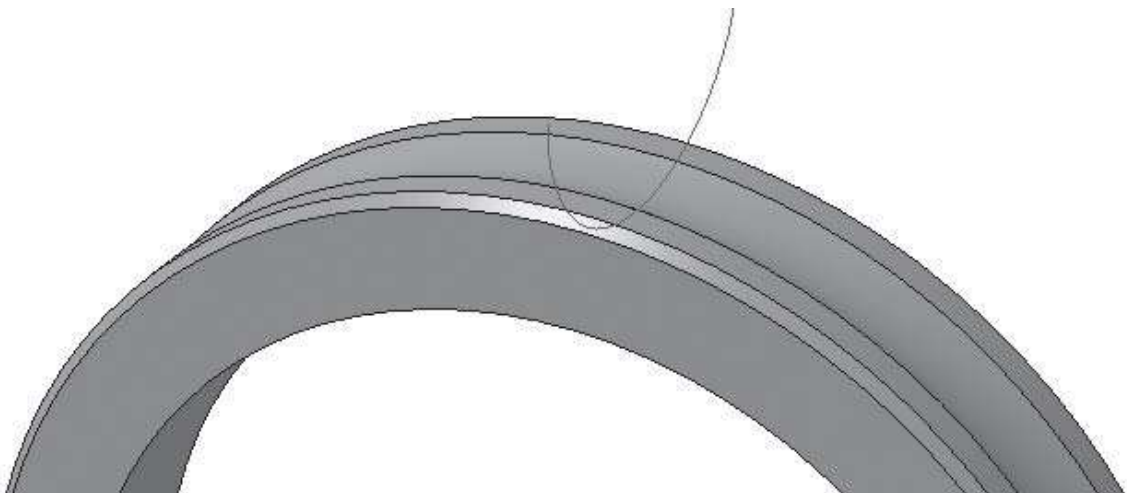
Напрямна для вирізування зубів черв'ячного колеса
